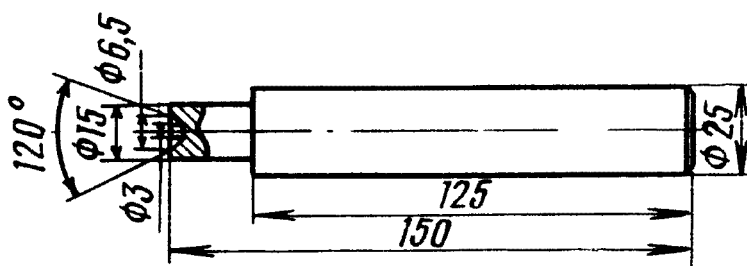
Приспособление для разборки и сборки перепускного клапана насоса гидроусилителя рулевого управления
